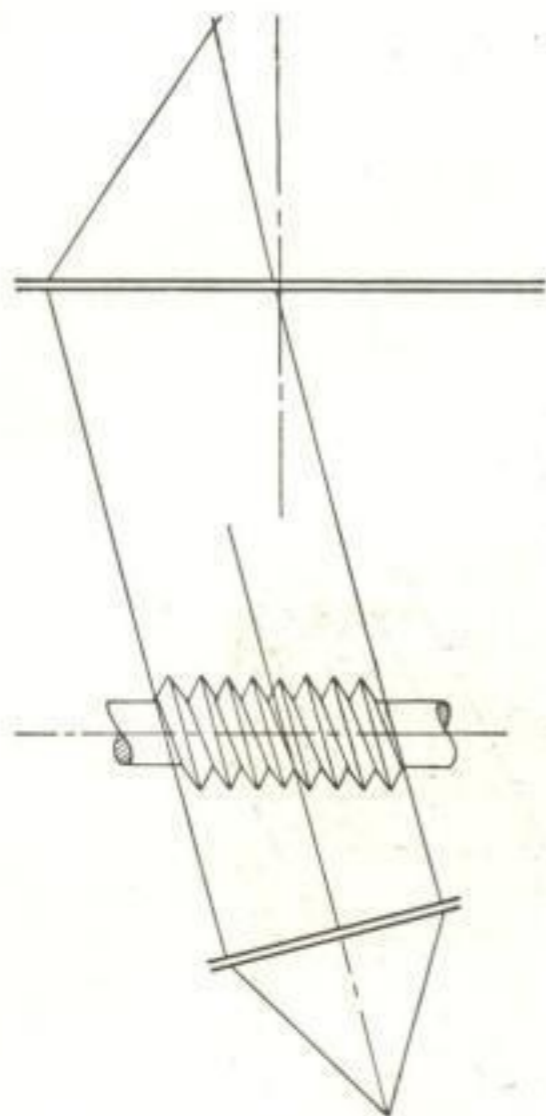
Korrekte Beleuchtung eines Gewindebolzens.
